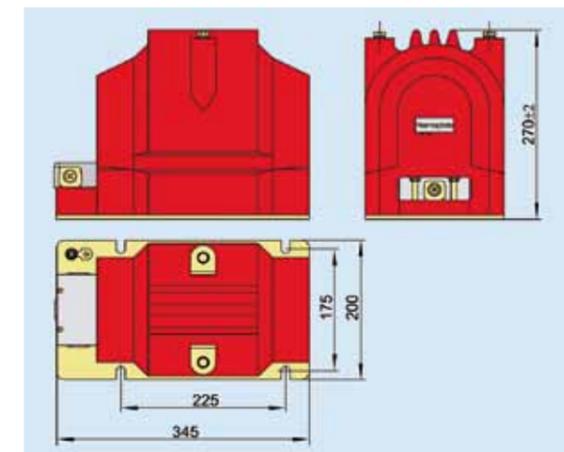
Внешний вид и размеры трансформатора напряжения JDZX11-10AG
